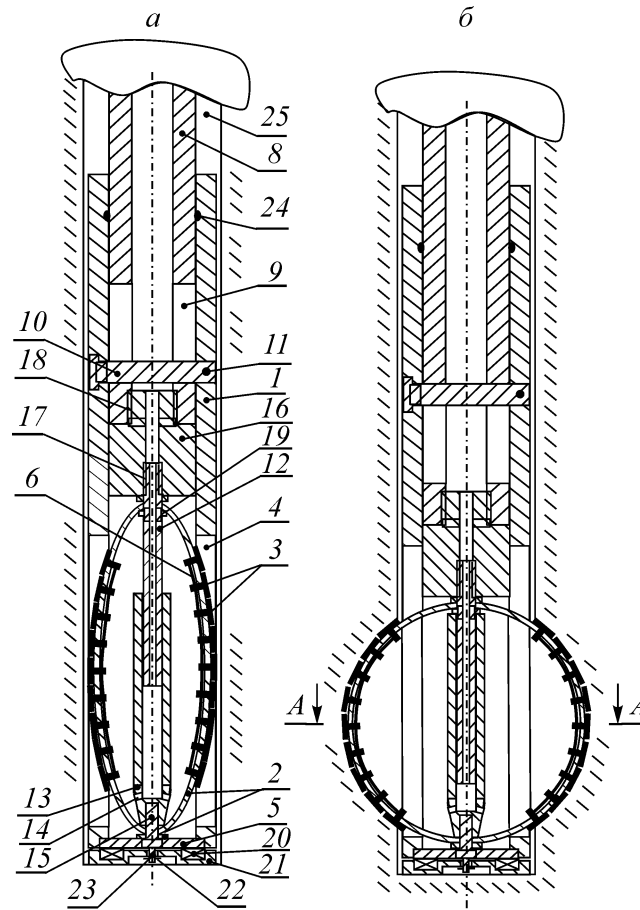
Образователь шаровых полостей— в исходном положении (а) и в момент окончания формирования полости (б): 1 — корпус; 2 — упругие пластины; 3 — вставки; 4 — продольные прорези; 5 — опора; 6 — проволока; 8 — труба; 9 — продольные прорези; 10 — стержень; 11 — шпилька; 12 — трубка; 13 — стакан; 14 — отверстия; 15 — выступ; 16 — втулка; 17 — резьба; 18 — резьба; 19 — выступ; 20 — подшипник; 21 — обойма; 22 — шпилька; 23 — выступ; 24 — кольцо; 25 — скважина
